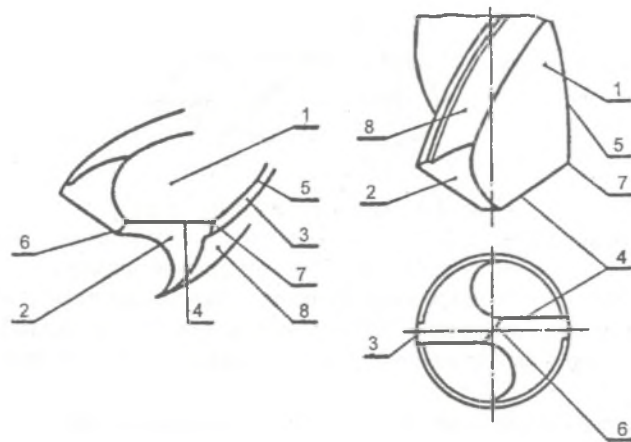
Поверхности лезвий сверла и его режущие кромки
